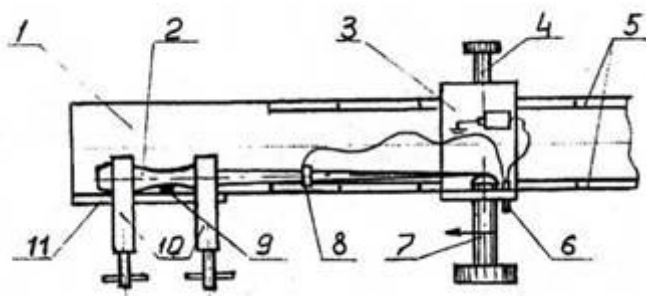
Устройство для испытания клинкового холодного оружия на прочность и упругость:
